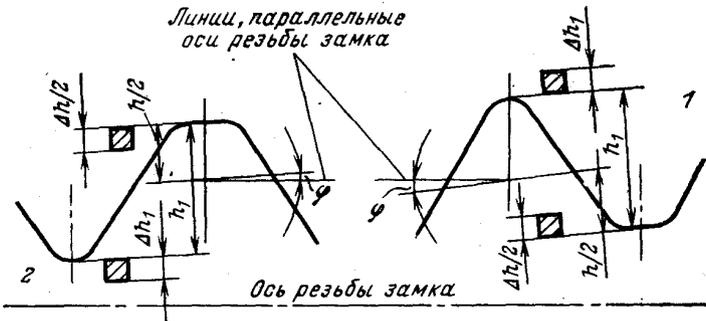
Схема расположения допусков при контроле высоты профиля замковой резьбы:
